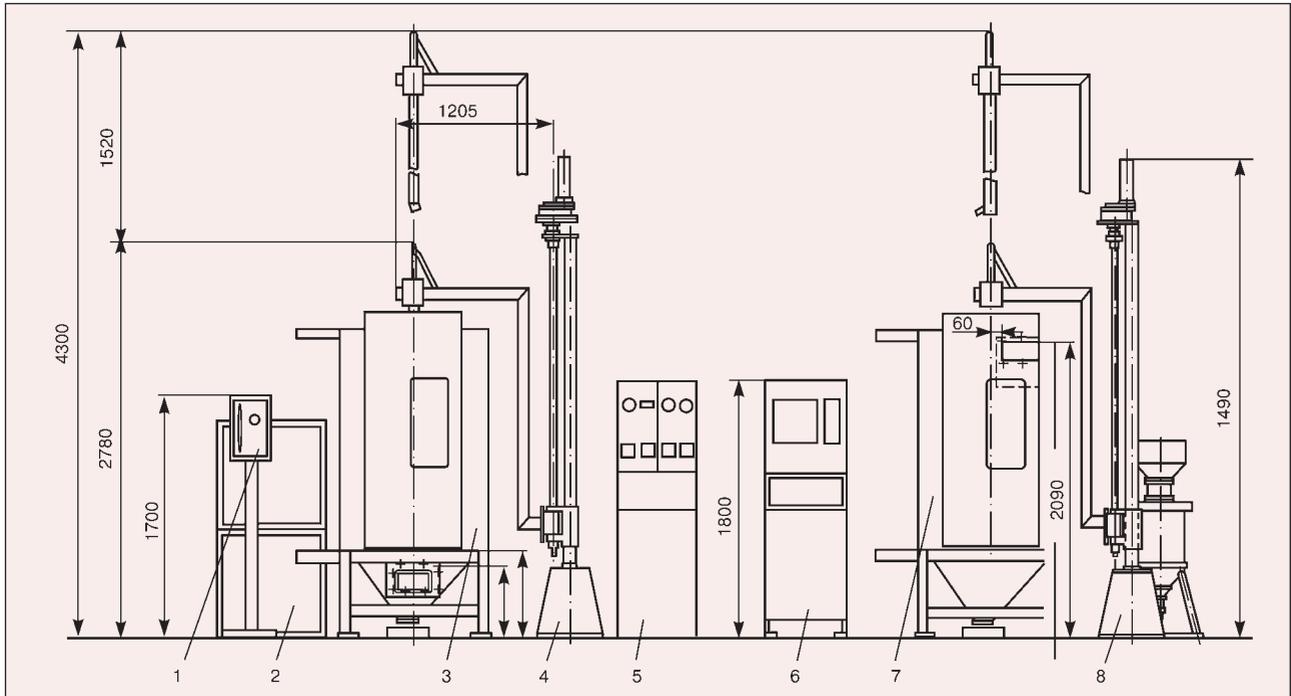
Схема линии плазменного напыления покрытий PLAZER ISS-75-PL на рабочие поверхности гильз судовых и локомотивных двигателей
